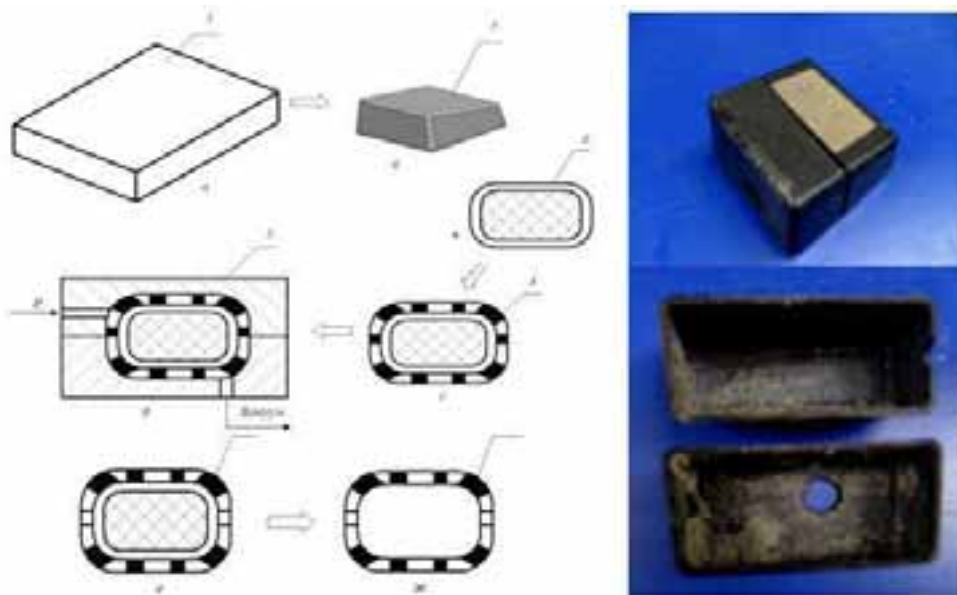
Схема изготовления композитной детали с замкнутой полостью с помощью вымываемого вкладыша: *a* – заготовка из материала Aquasore; *б* – фрезерованный вкладыш; *в* – вкладыш со слоем изоляции; *г* – подготовка преформы; *д* – формование методом RTM; *е* – извлечение детали и сверление отверстия; *ж* – готовая деталь с замкнутой полостью; *з* – деталь в разрезе
